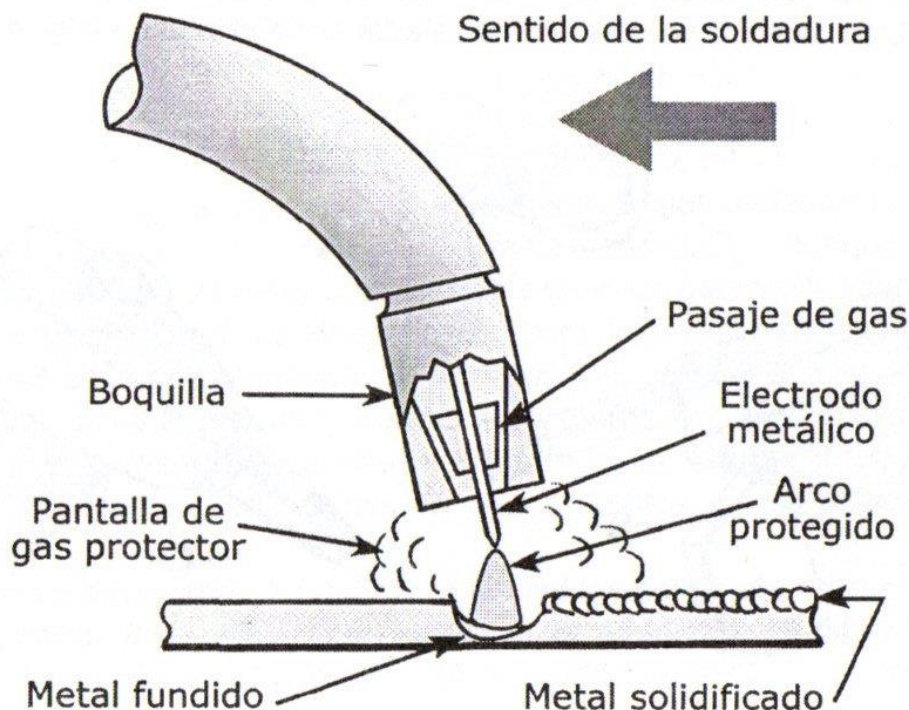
Ilustración de los efectos producidos en una soldadura MIG
